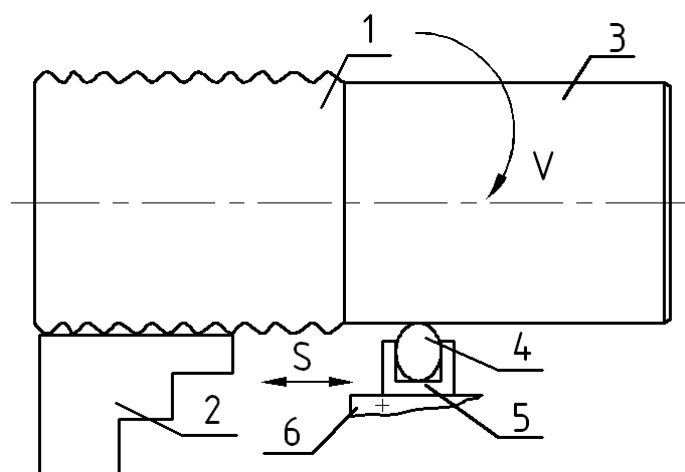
Схема пластического деформирования поверхностного слоя для уменьшения шероховатости:
